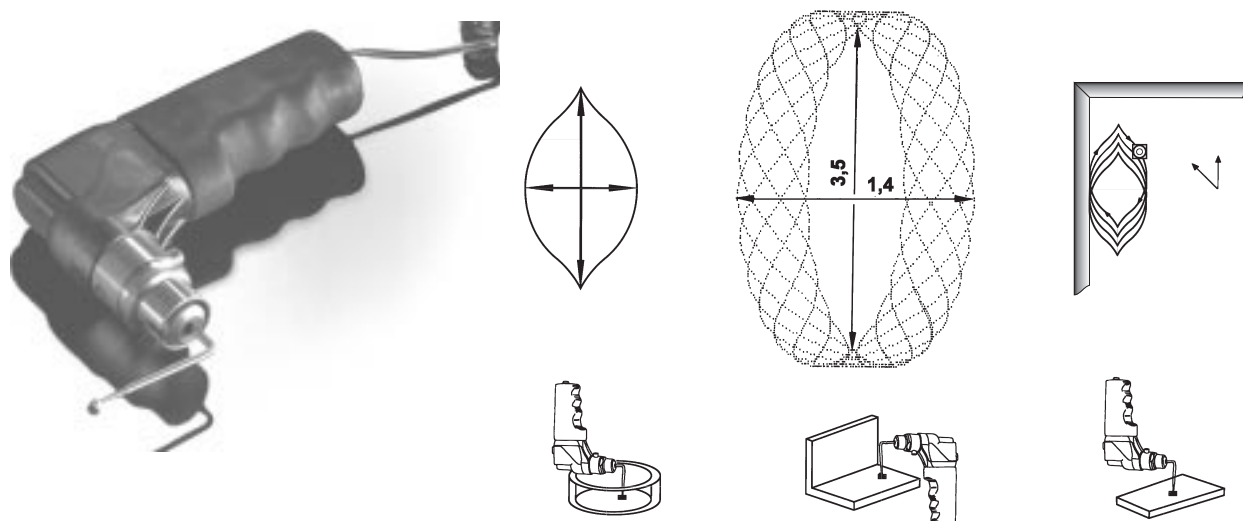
Осциллирующий привод ORBITOR и схема движения рабочего органа.
